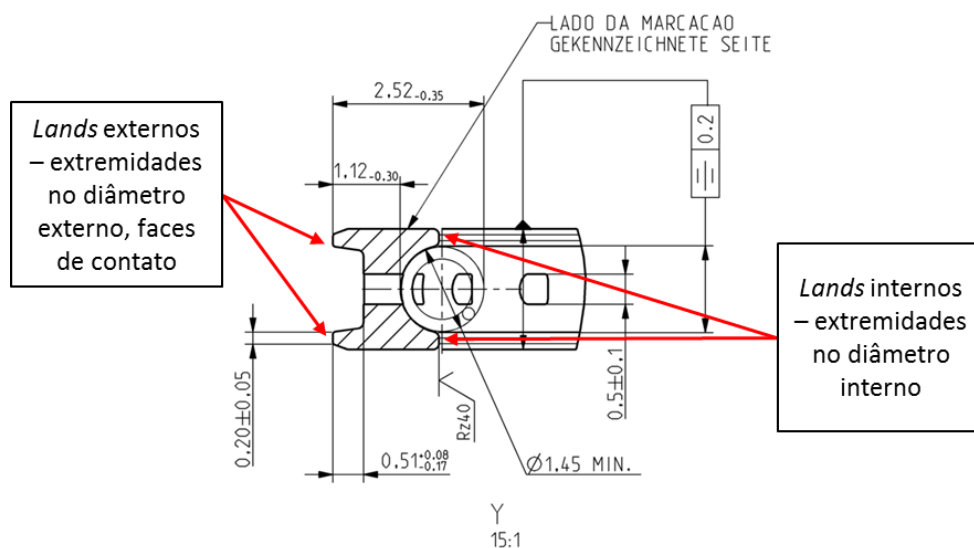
Indicação dos locais mais suscetíveis para a fissuração no anel *I-Shaped*. Recorte do desenho técnico do perfil do tipo de anel *I-Shaped* em estudo [3].
